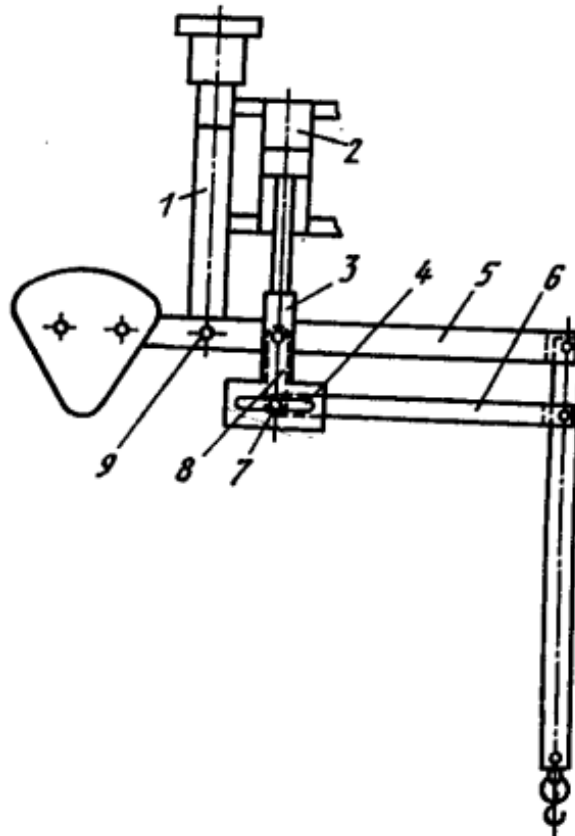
Схема збалансованого маніпулятора із приводом на поворотній колоні: 1 – поворотна колона; 2 – привод; 3 – Т-образна вилка; 4 – куліса; 5, 6, 8 – важелі; 7 – ролики; 9 – шарнір.
